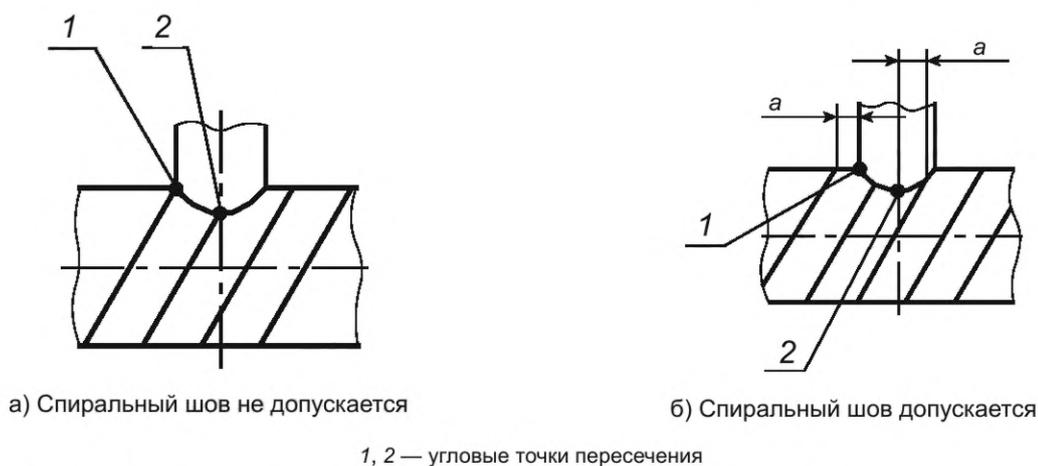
Сварка патрубков (штуцеров) с трубопроводами со спиральными швами
